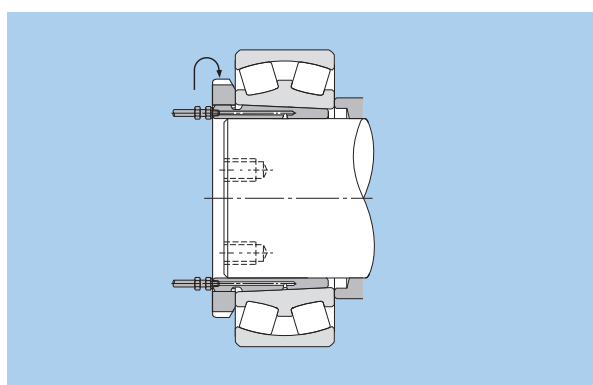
Extração utilizando uma bucha hidráulica de desmontagem
